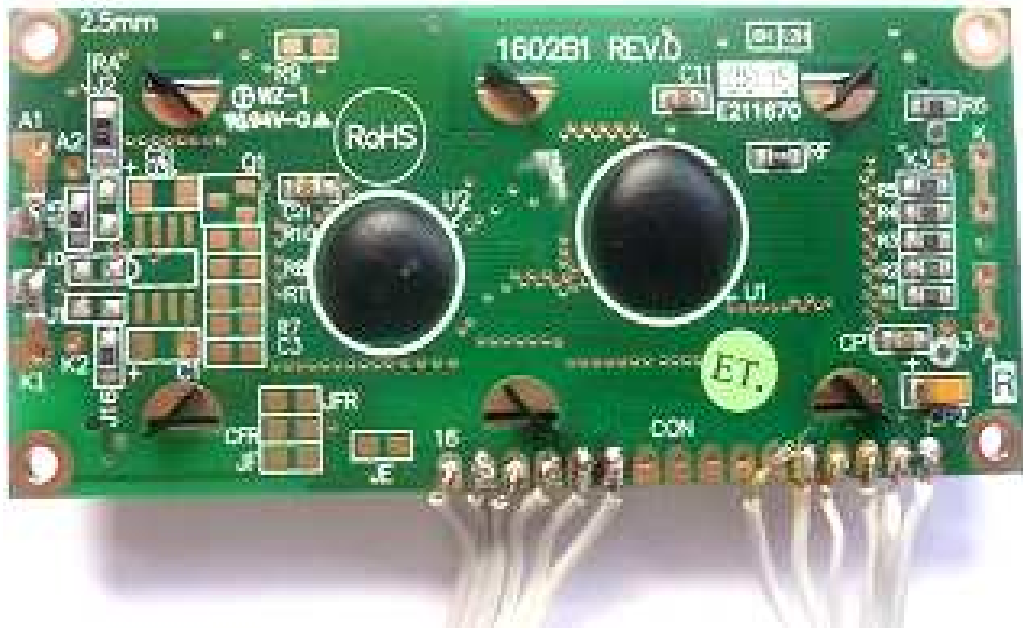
Soldadura del cable Ribbon a la pantalla LCD
